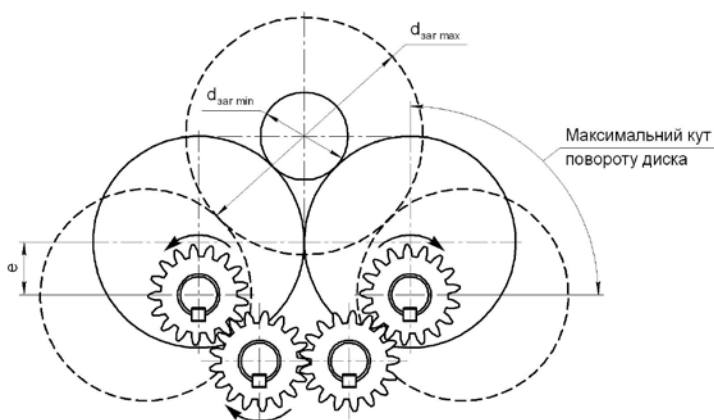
Схема механізму регулювання установочних елементів базуючої призми (патент України № 31416)
